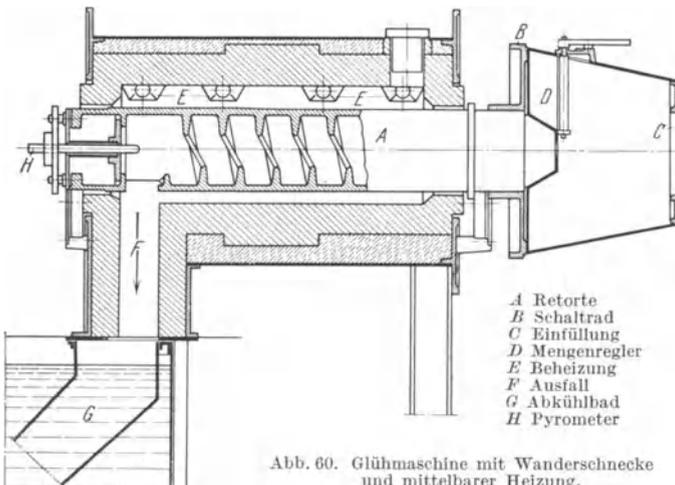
Glühmaschine mit Wanderschnecke und mittelbarer Heizung.
